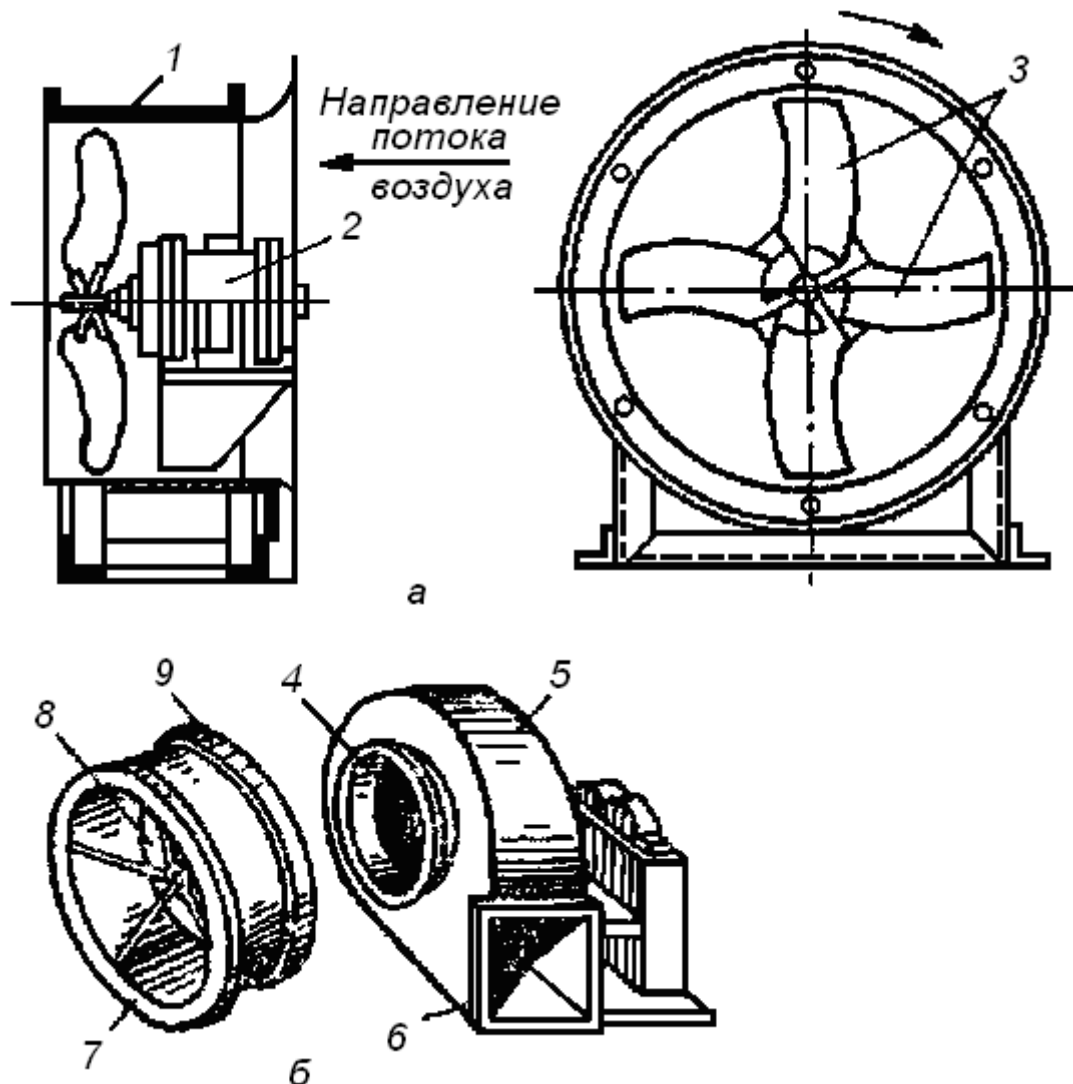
Вентиляторы: а – осевой; б – радиальный: 1 – обечайка; 2 – электродвигатель; 3 – лопатки рабочего колеса; 4 – всасывающее отверстие; 5 – улиткообразный кожух; 6 – вал; 7 – нагнетательный патрубок; 8 – переднее кольцо; 9 – ступица; 10 – основной диск
